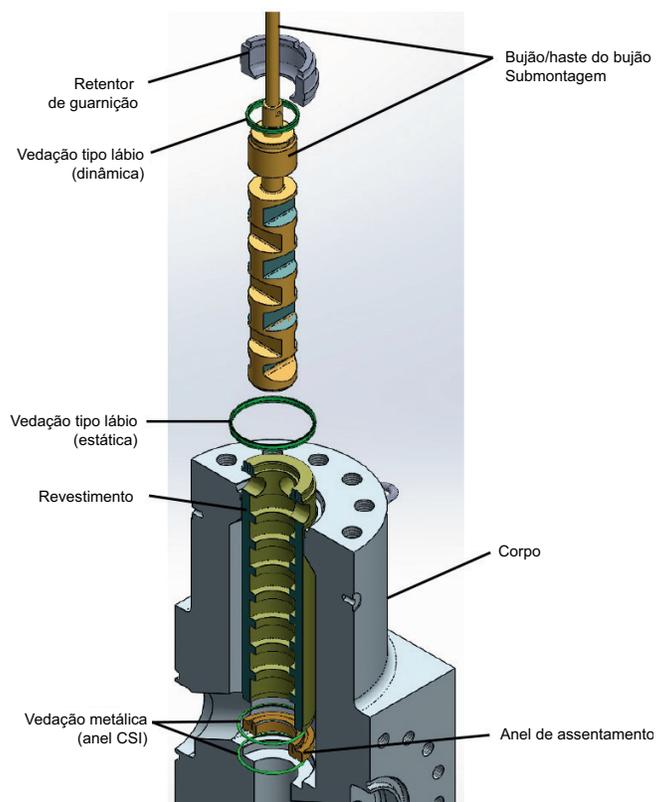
Vista explodida do conjunto de guarnição - revestimento integral/anel de assentamento (desequilibrado 1")
